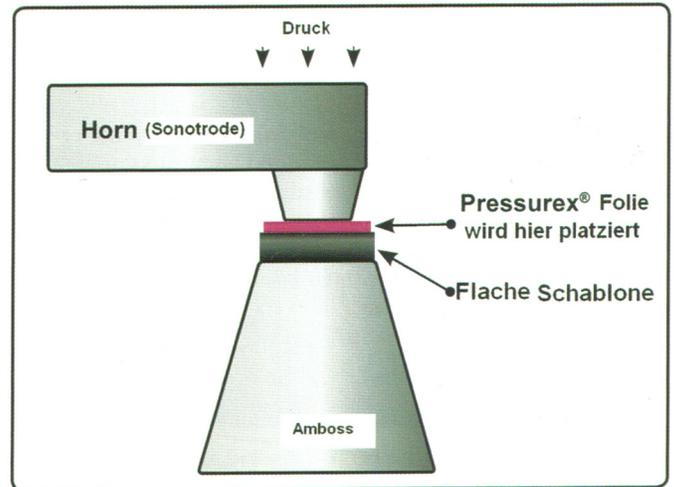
Pressurex® im Einsatz bei der Ultraschallschweißung
